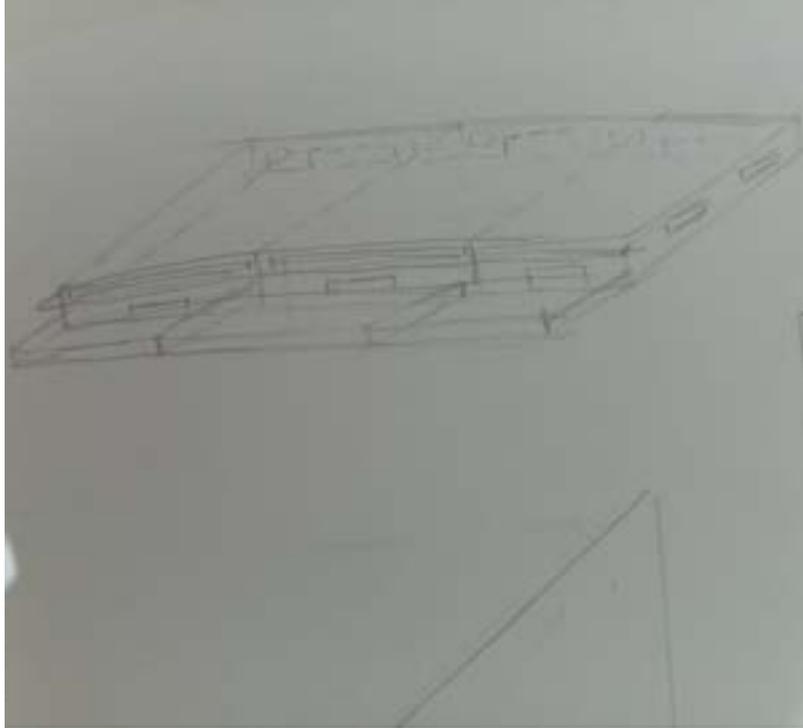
Croqui conceito da vista posterior do bloco de entrada
